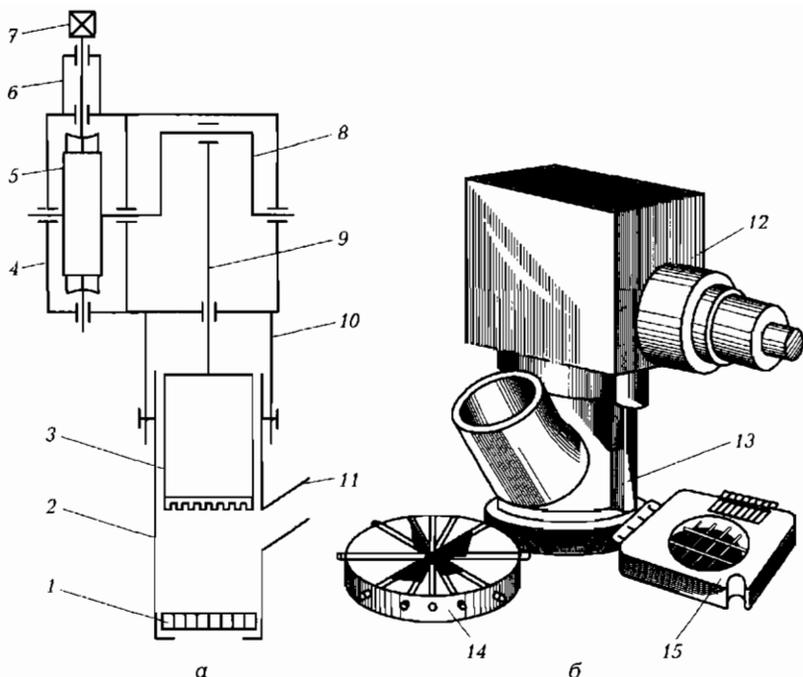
Сменный механизм для нарезания сырых овощей МС28-100: а — кинематическая схема; б — общий вид; 1 — ножевая решетка; 2 — цилиндр; 3 — поршень; 4 — редуктор; 5 — червячная передача; 6 — стакан; 7 — хвостовик вала; 8 — коленчатый вал; 9 — шток; 10 — соединительная тяга; 11 — загрузочная воронка; 12 — загрузочный бункер; 13 — рабочая камера; 14 — цилиндрическая решетка; 15 — прямоугольная решетка
